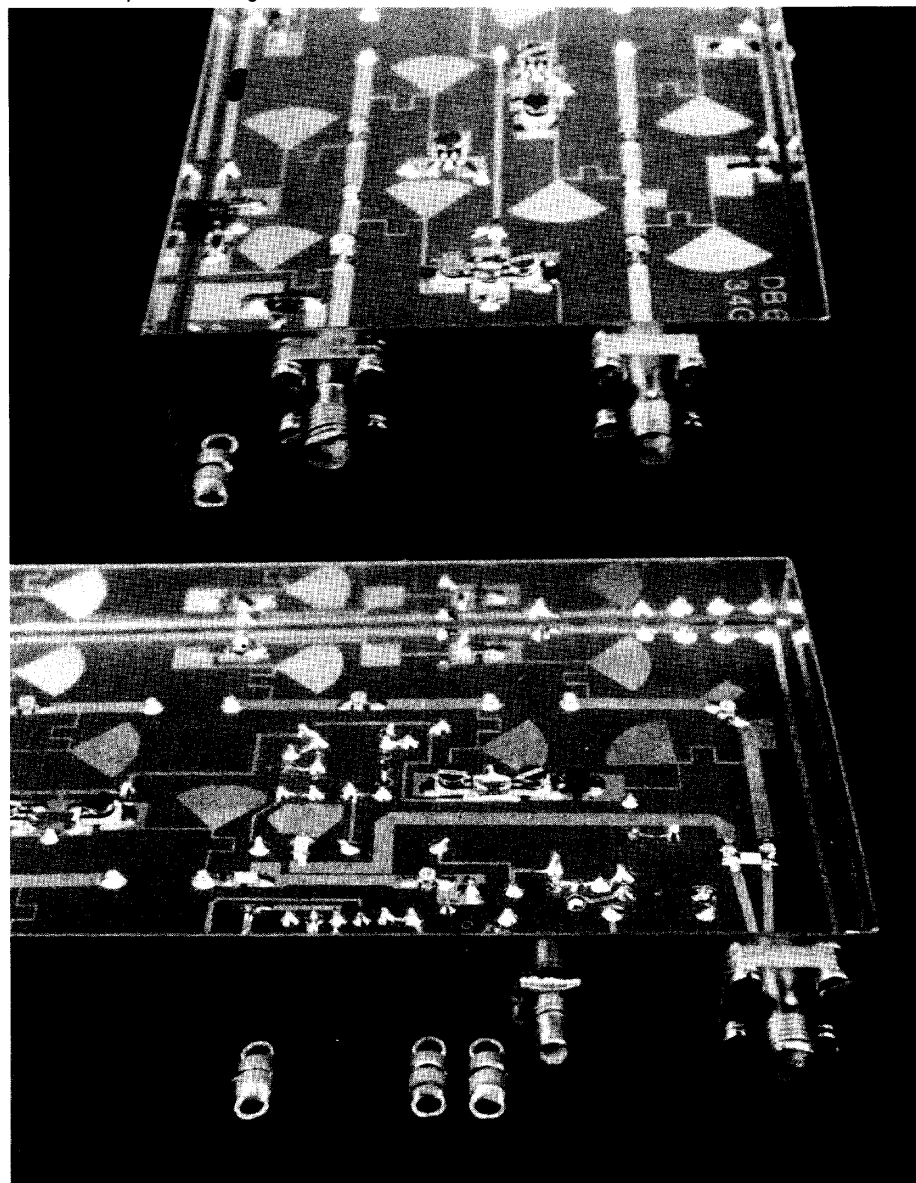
De gemonteerde transvertor in de doos. Bovenaan de uitgangszijde, onderaan de ingang.
